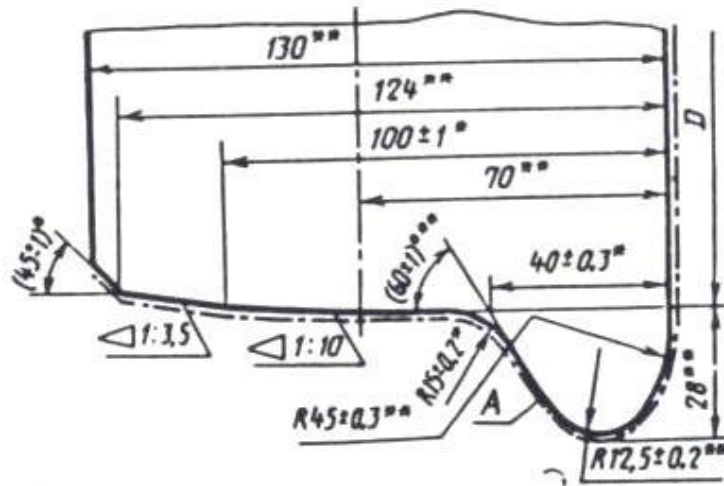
Стандартний профіль поверхні обода колеса
